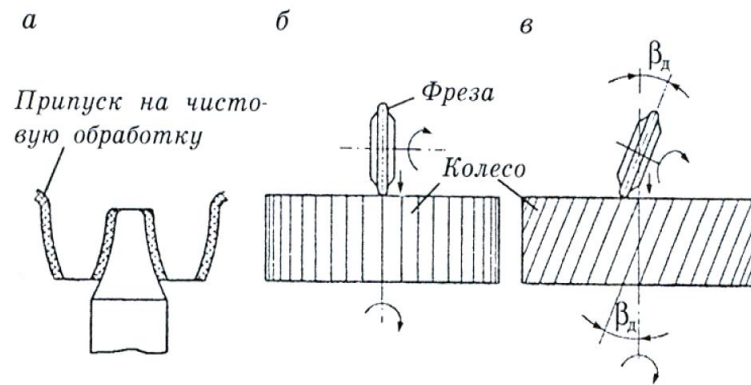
Нарезание зубьев модульными дисковыми фрезами: а – профиль зуба фрезы и впадины зубчатого колеса; б – схема нарезания прямозубых колес; в – схема нарезания косозубых колес
